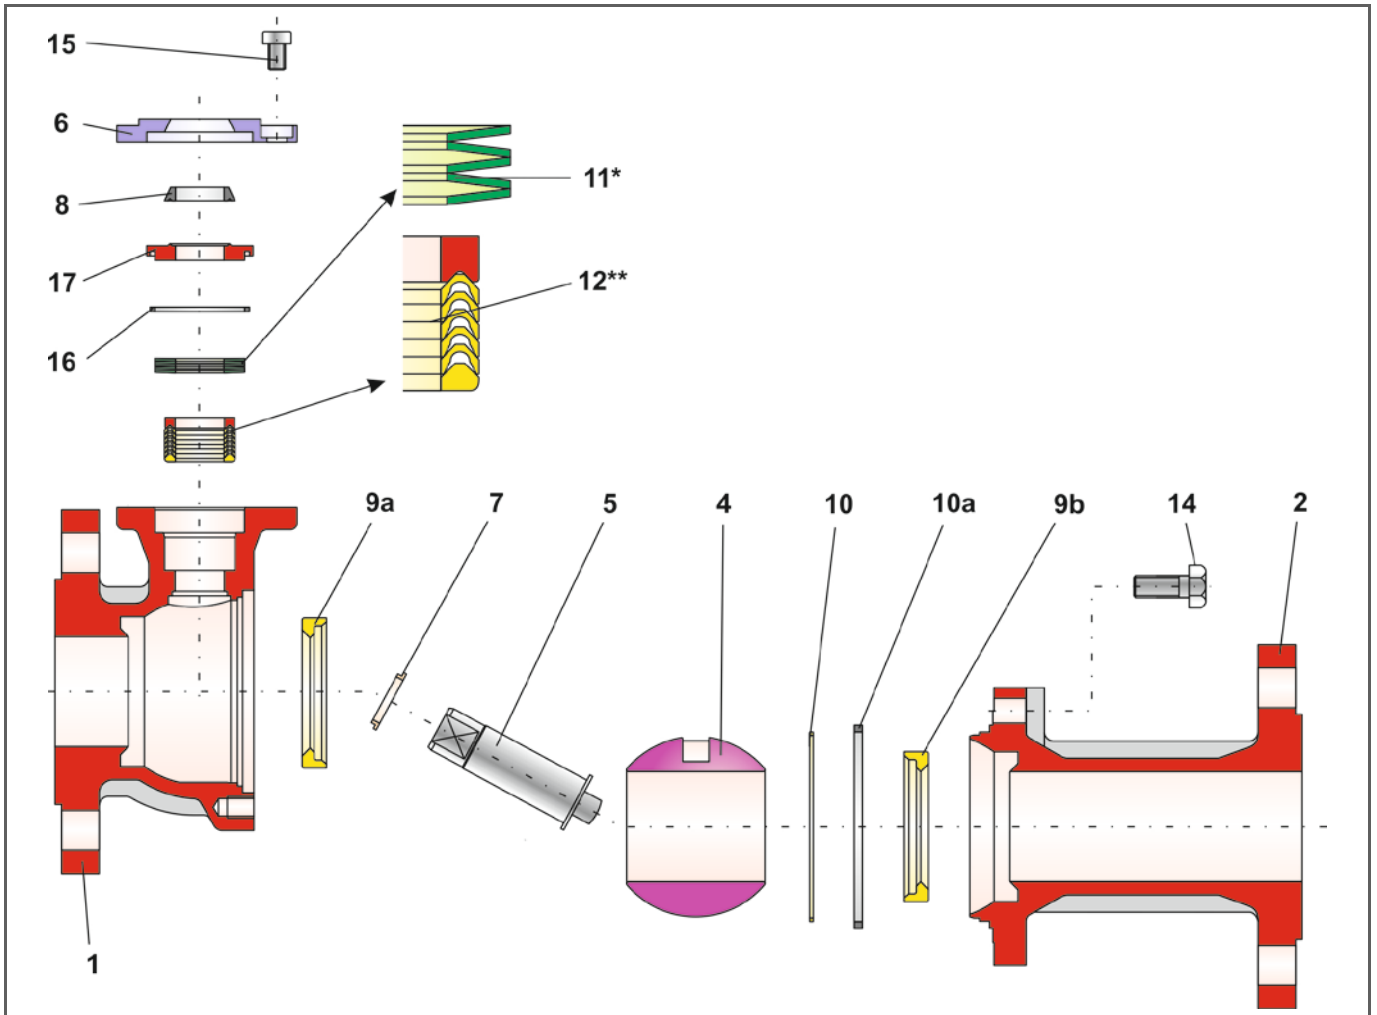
Explosionszeichnung des Kugelhahns BR 26d, Fire Safe Ausführung
